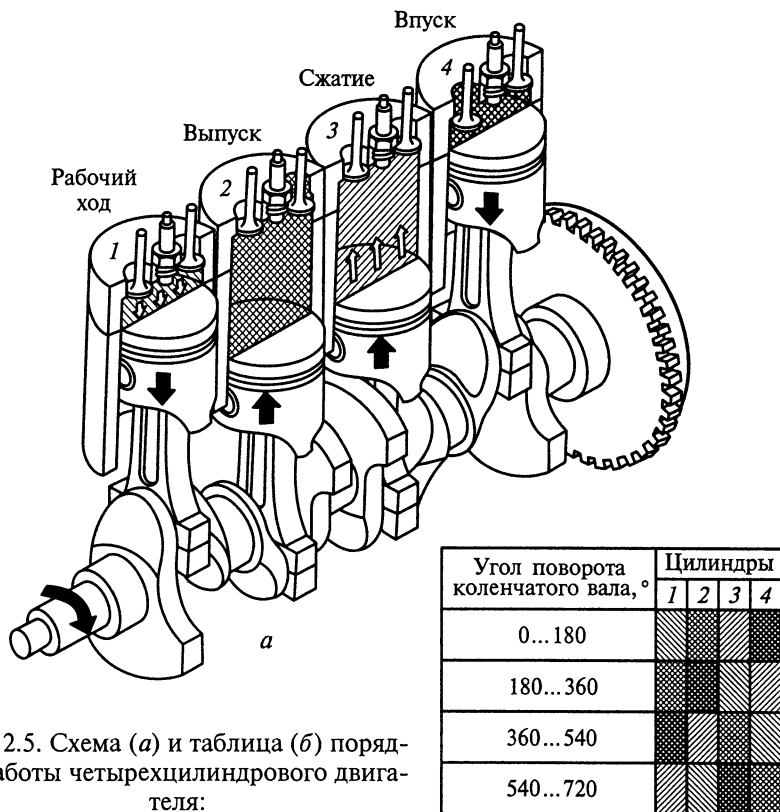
Схема (а) и таблица (б) порядка работы четырехцилиндрового двигателя:
